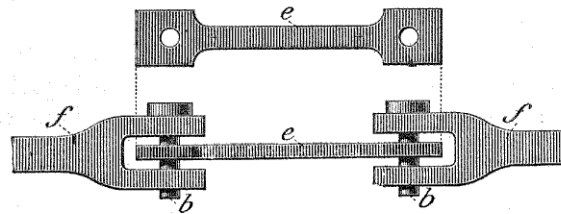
Mode d'attache des éprouvettes pour tôles.
